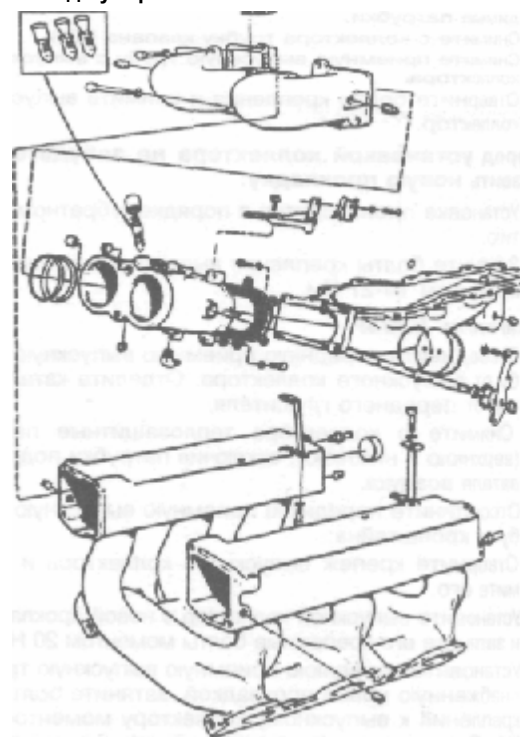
Впускной коллектор в сборе • • Двигатель B280F 1
